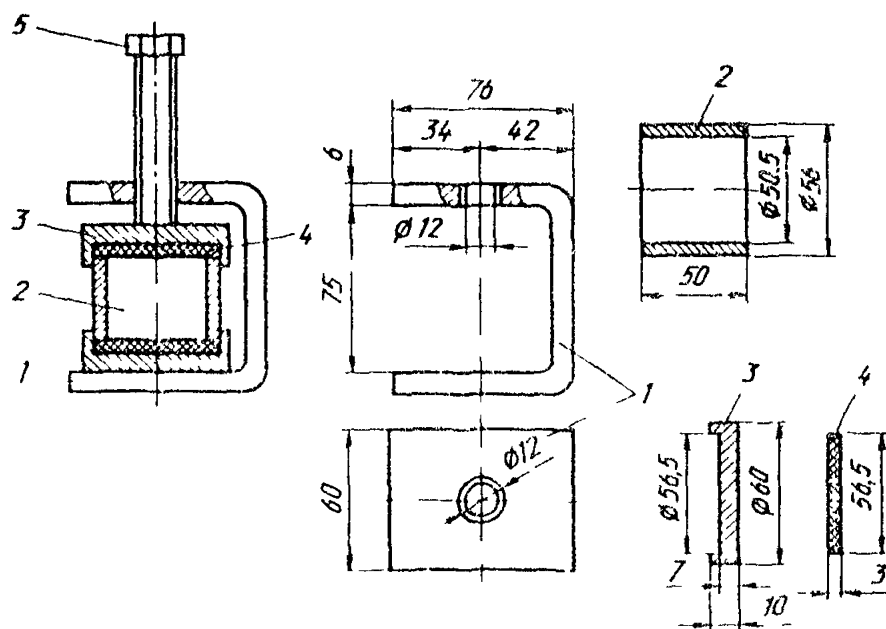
Обойма для прогрева цементогрунтовых образцов: 1 - струбина; 2 - кольцо; 3 - крышка; 4 - резиновая прокладка; 5 - болт
